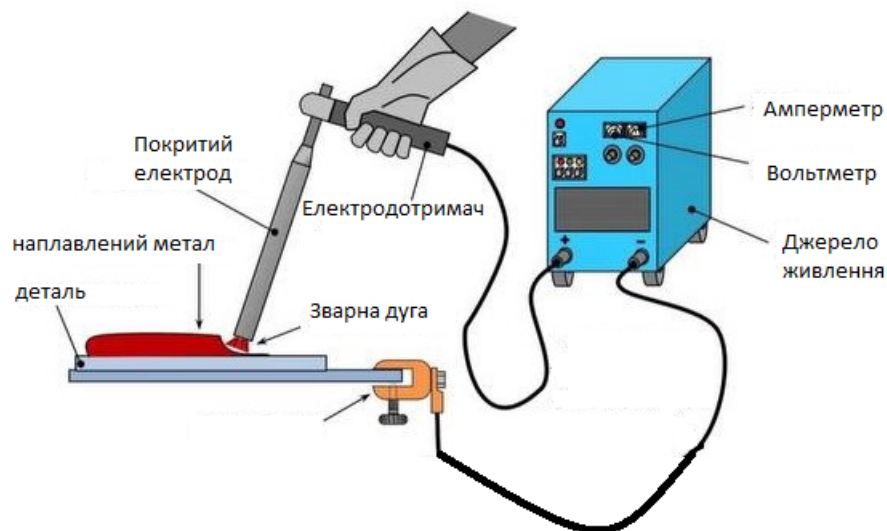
Схема ручного дугового наплавлення покритими електродами [12]
